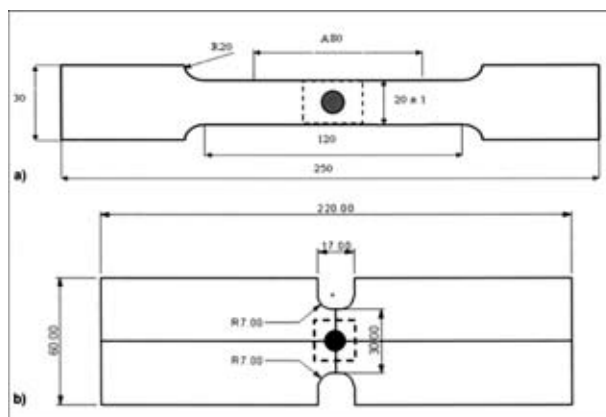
Форма образцов для различных видов испытаний точечного сварного соединения: а — одноосное растяжение; в — двухосное напряжение
